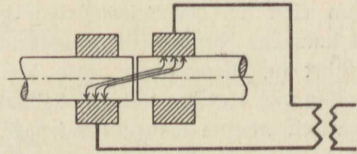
Stromzuführung beim Stumpfschweißen.
